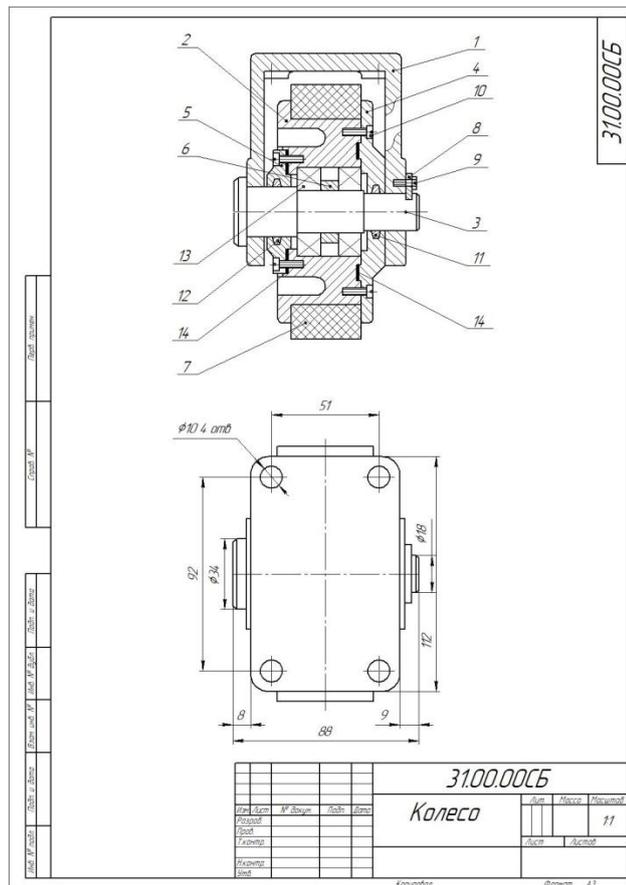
Образец выполнения задания КГ4: сборочный чертеж
